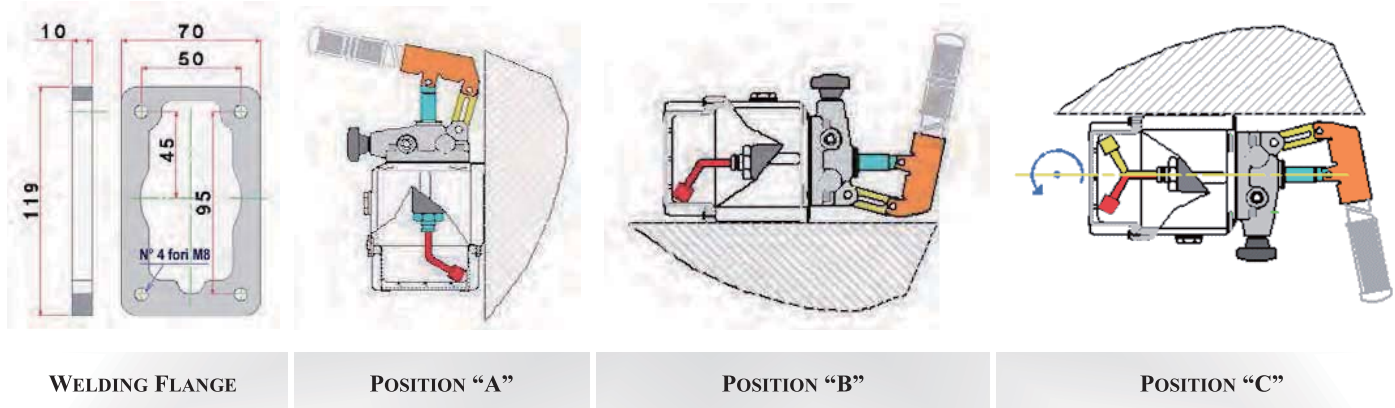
(FLANGIA A SALDARE - POSIZIONE TUBO ASPIRAZIONE) - PICTURE 4 (WELDING FLANGE - SUCTION PIPE POSITION)
